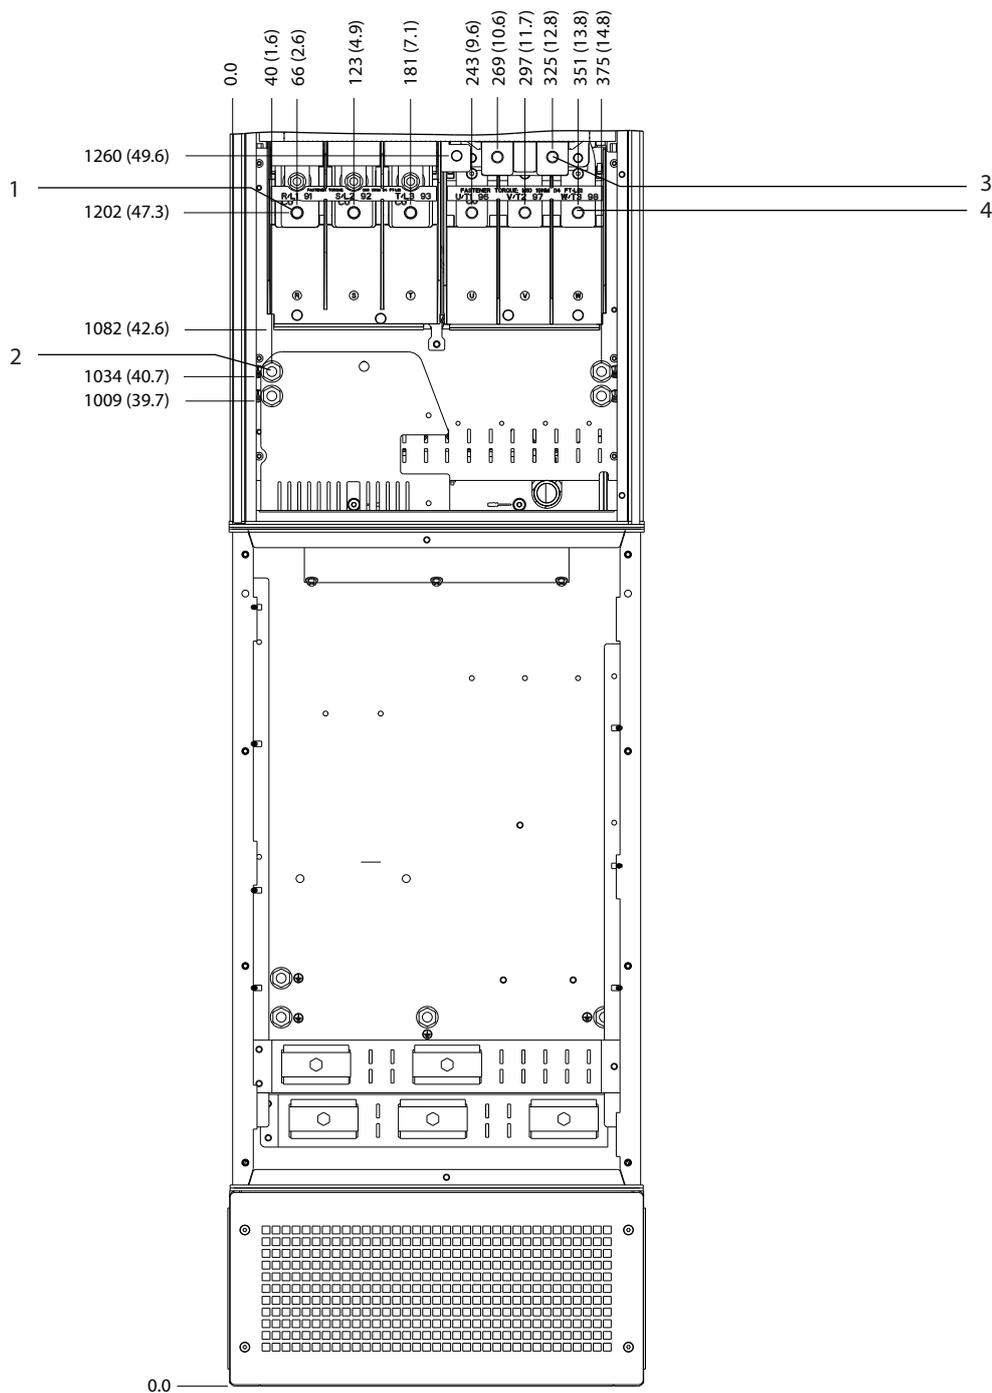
Dimensões do terminal do D7h com opcional de desconexão (vista frontal)
